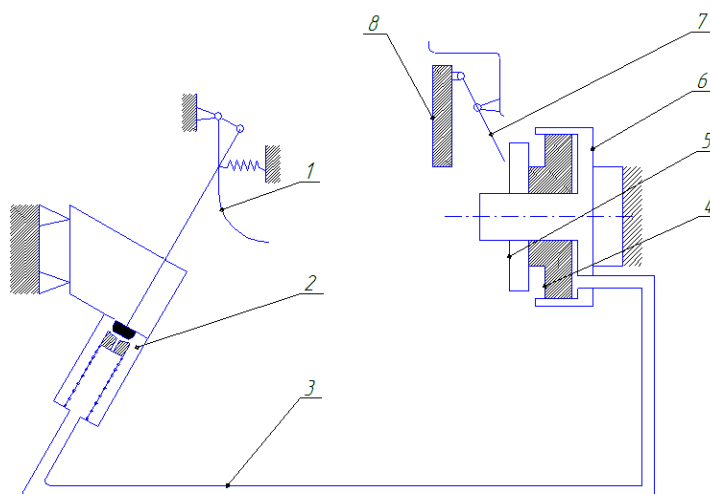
Предлагаемая схема привода сцепления автомобиля КамАЗ: 1 - педальный привод; 2 - главный гидроцилиндр; 3 - гидролиния; 4 - силовой гидроцилиндр; 5 - выжимной подшипник; 6 - корпус; 7 - отжимной рычаг; 8 - нажимной диск;
